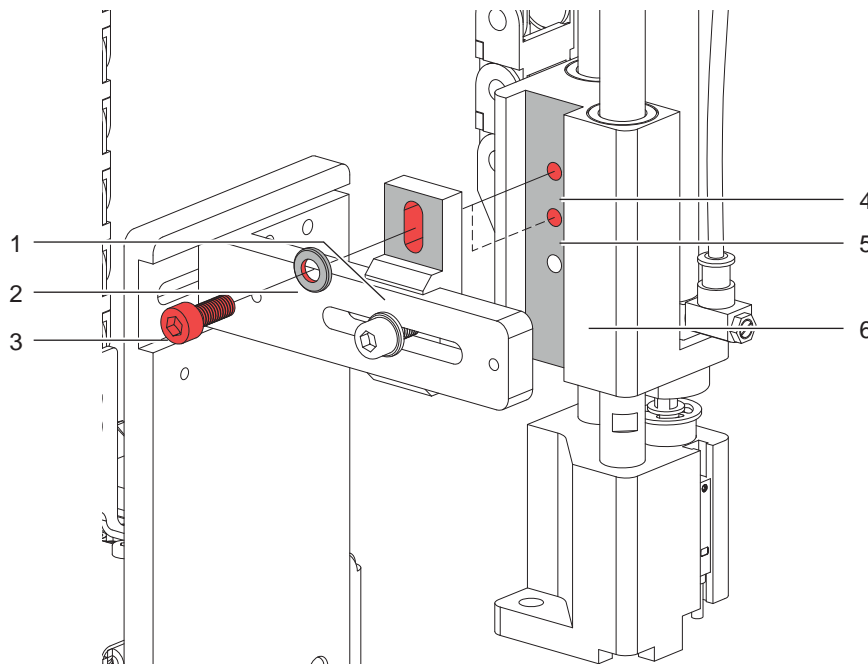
Umbau für Einsatz des Stempeltyps A1321
